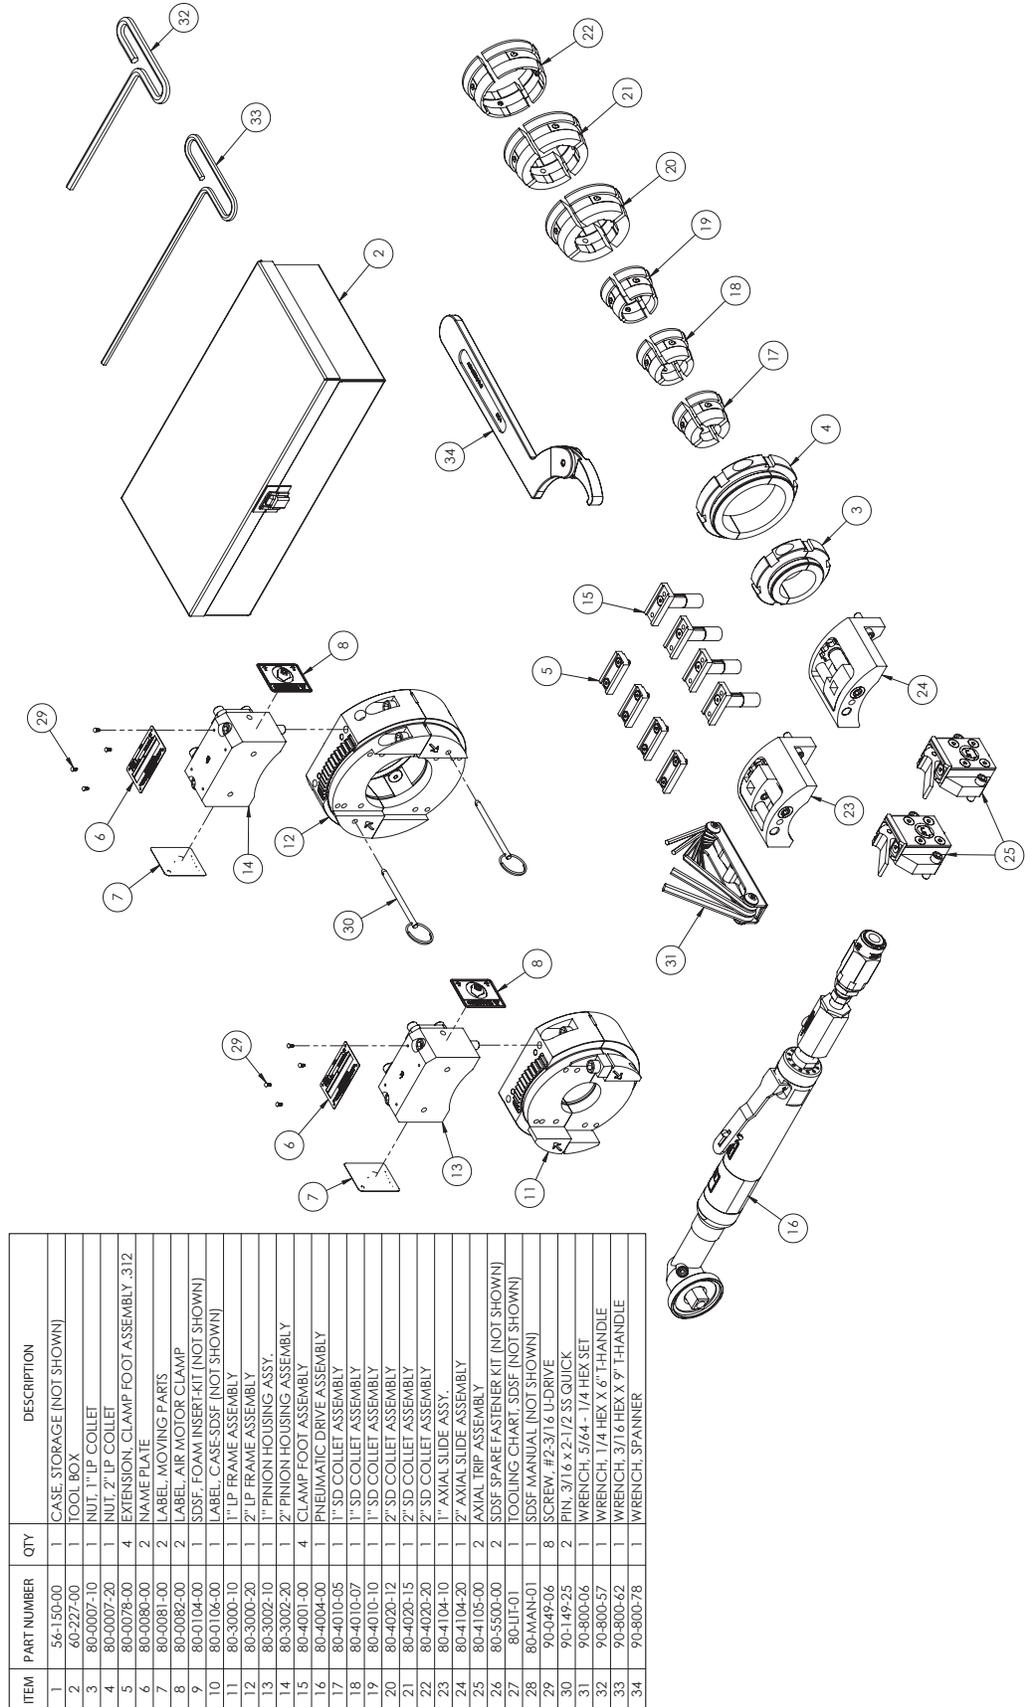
El portaherramientas axial para soldadura por encastre (80-4104-XX) utiliza un ensamble de desenganche axial (80-4105-00).
